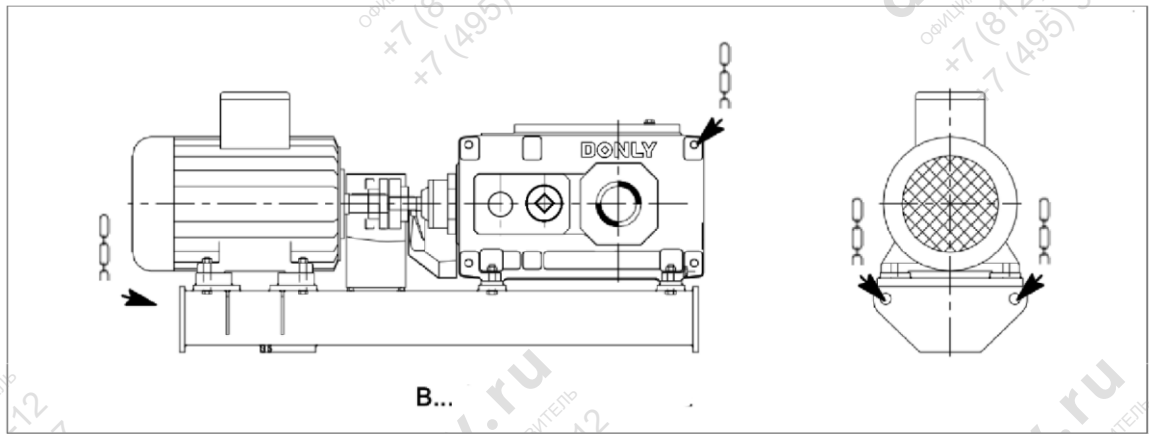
Расположение точек крепления на редукторах типа ВЗ.Н со вспомогательным приводом
